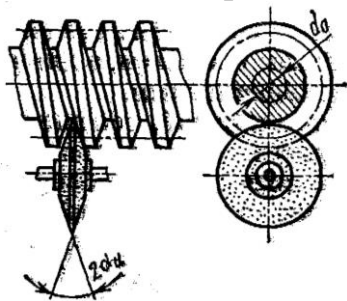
Схема шліфування евольвентного черв'яка дисковим кругом
